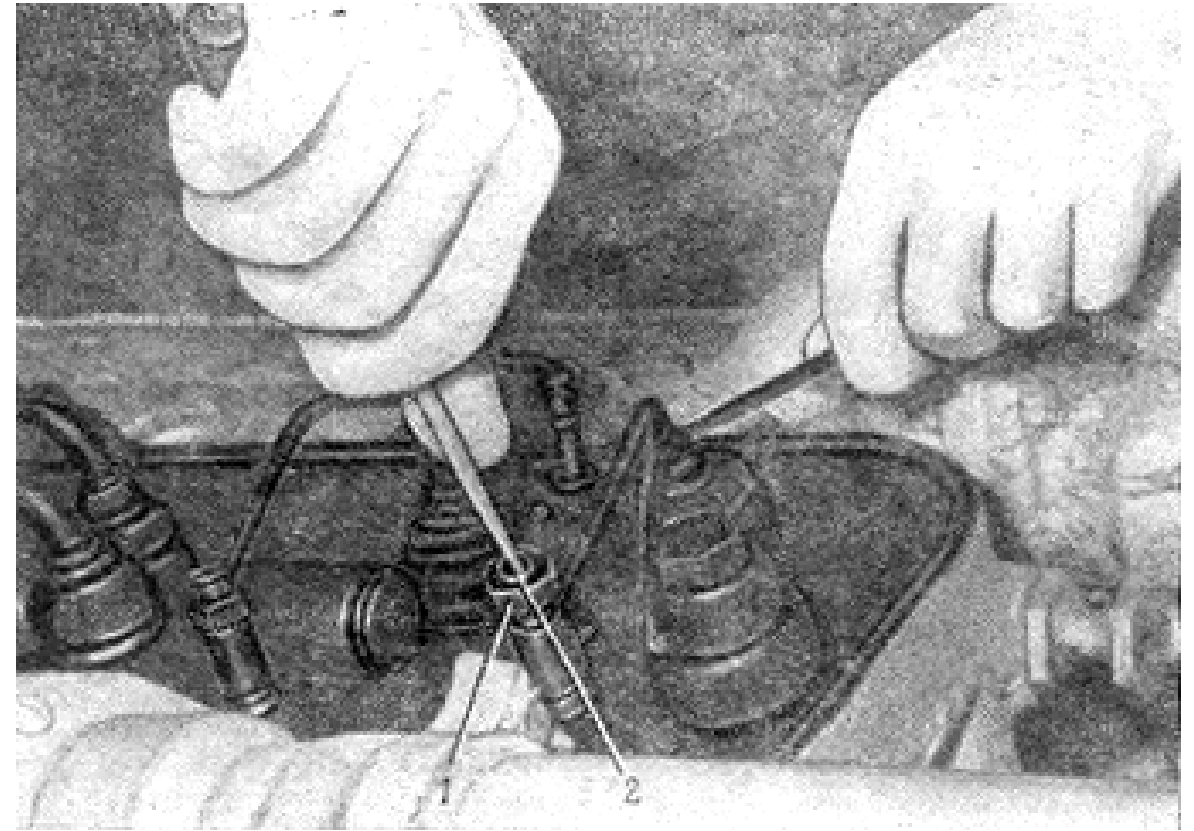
Регулировка зазоров клапанного механизма транспортера-тягача МТ-ЛБ:
